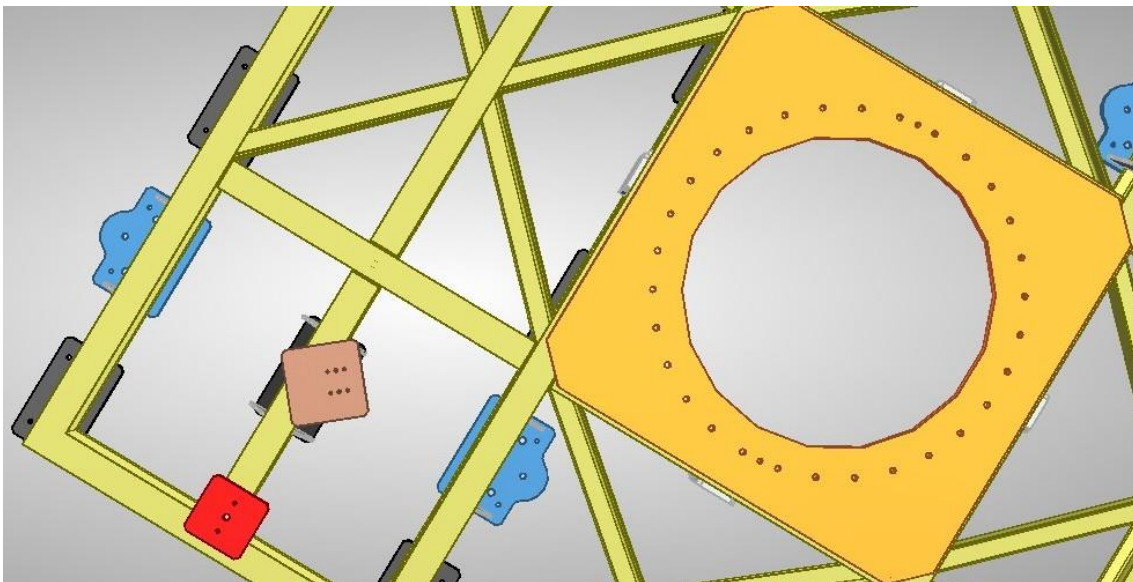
Vista inferior del bastidor, detalle de placa de apoyo, consola y placa de centraje
